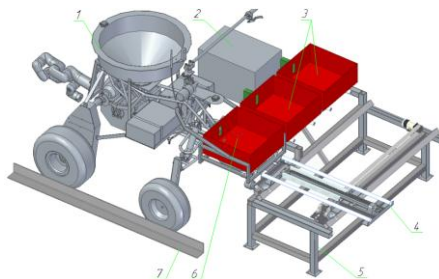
Схема станції автоматичної заміни батарей: 1 – робот; 2 – зарядний пристрій; 3 – запасні батареї; 4 – маніпулятор; 5 – рама; 6 – батарея робота; 7 – пристрій позиціонування
